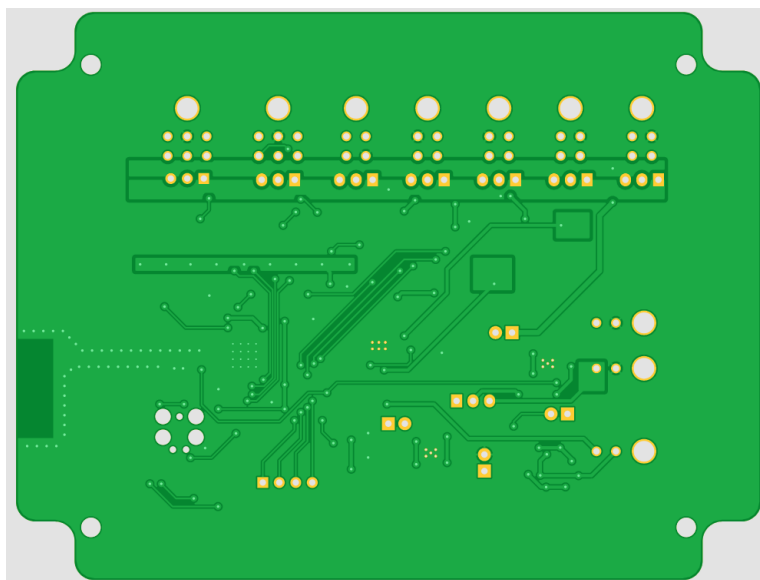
Desenho da PCB da Caixa de Sensores - Lado Inferior
